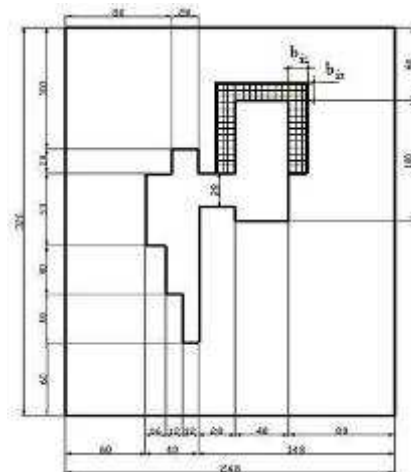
Dimensiunile ansamblului piesă turnată – formă
